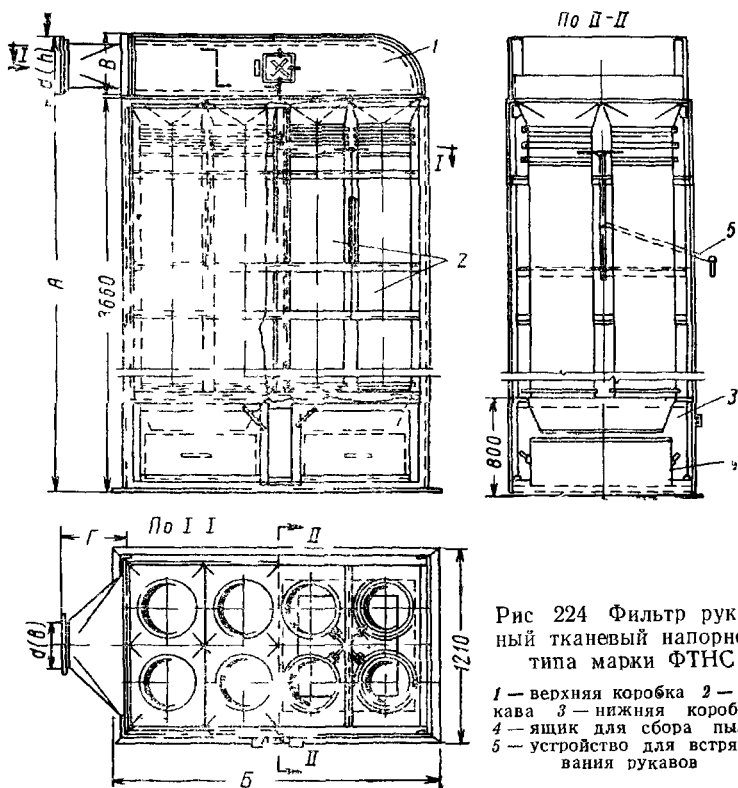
Фильтр рукавный тканевый напорного типа марки ФТНС
